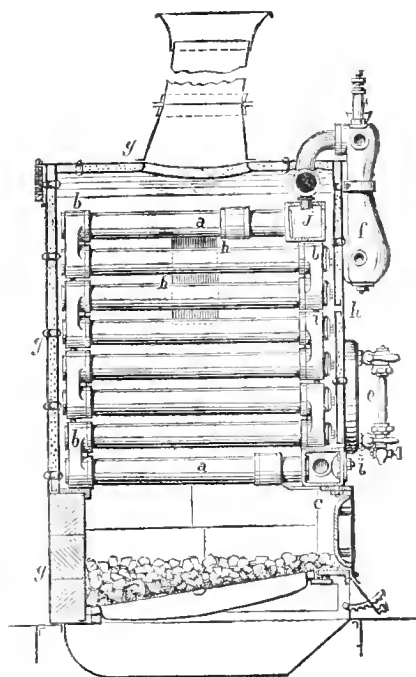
Coupe de la chaudière de la machine de M. Belleville.
